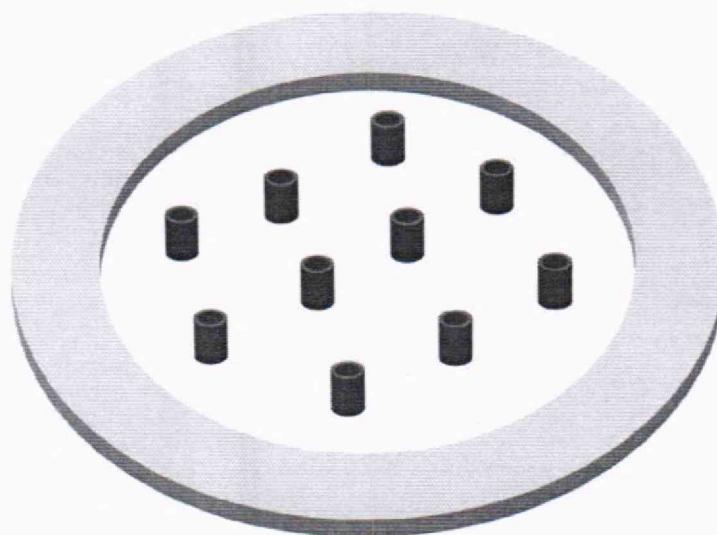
Схема установки алюминиевых втулок внутри вспомогательного кольца
